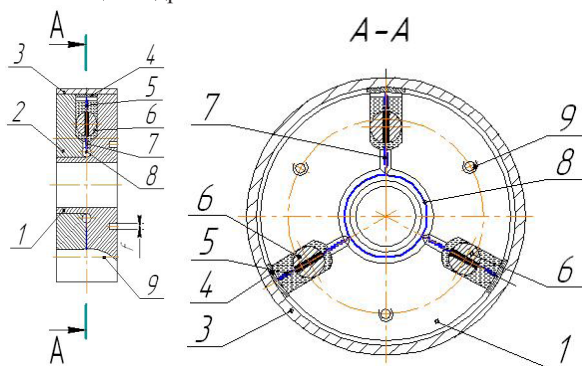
Общий вид устройства для автобалансировки заготовок
